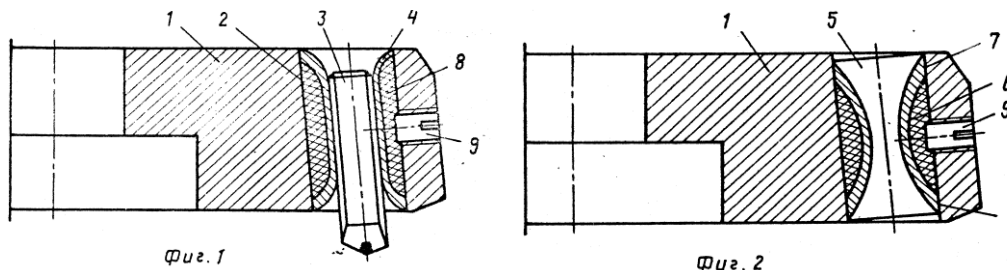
Торцева фреза по а. с. 1214343 МКИ В 23 С 5/06
